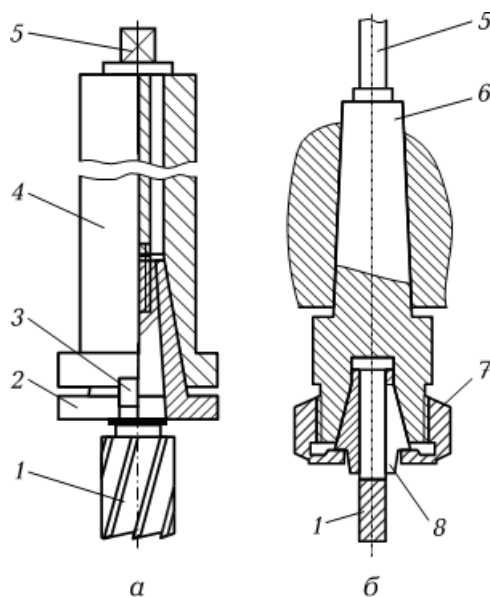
Схемы установки и закрепления на вертикально-фрезерном станке концевых фрез:
